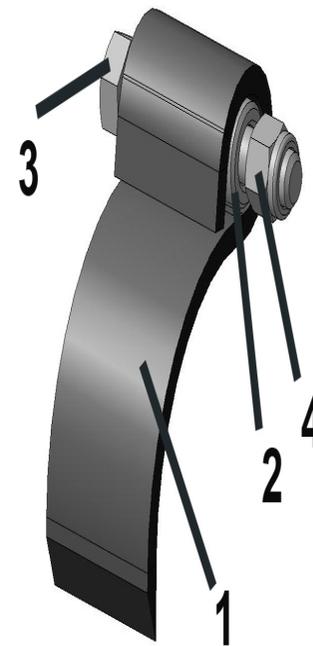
ИРО 03.500А Нож в сборе (длинный)
